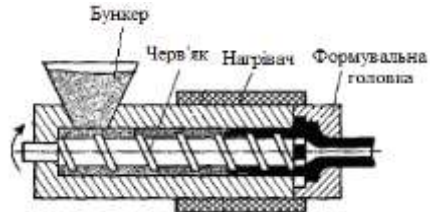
Схема черв'ячного екструдера для формування труб
